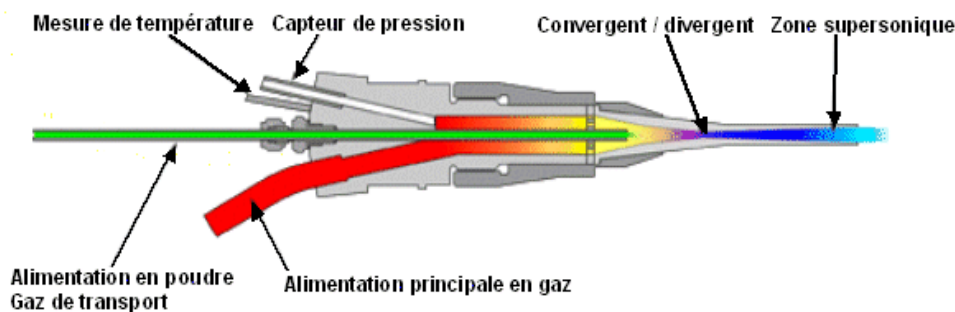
Schéma vu en coupe du pistolet cold spray
